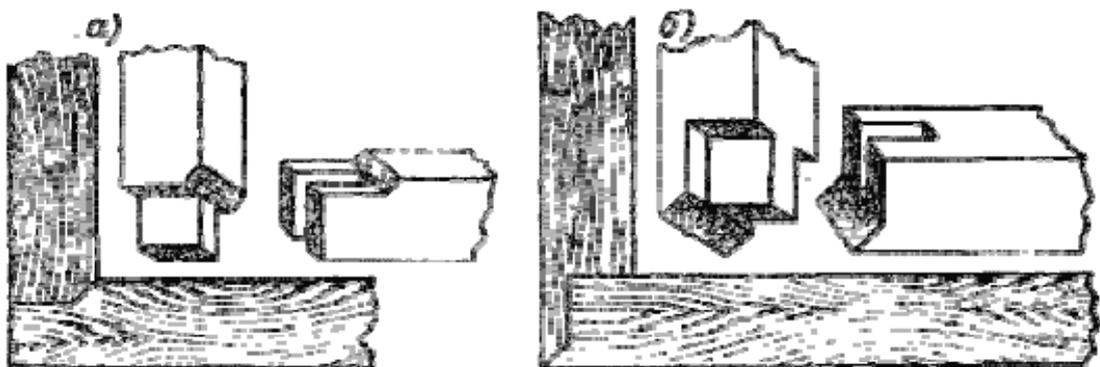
Вязка шипом с фальцем: а) калевка с внутренней стороны; б) калевка с наружной стороны.
